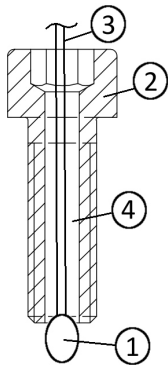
Modifizierte Schraube für die Temperaturmessung in der Brühgruppe
